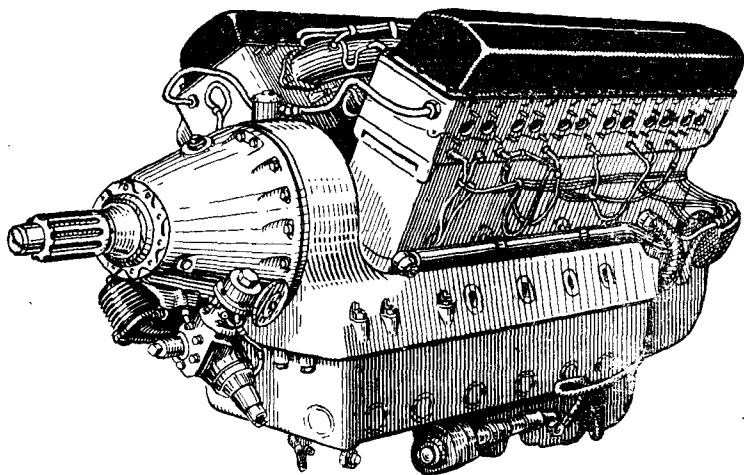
V-образный 12-цилиндровый авиадвигатель
